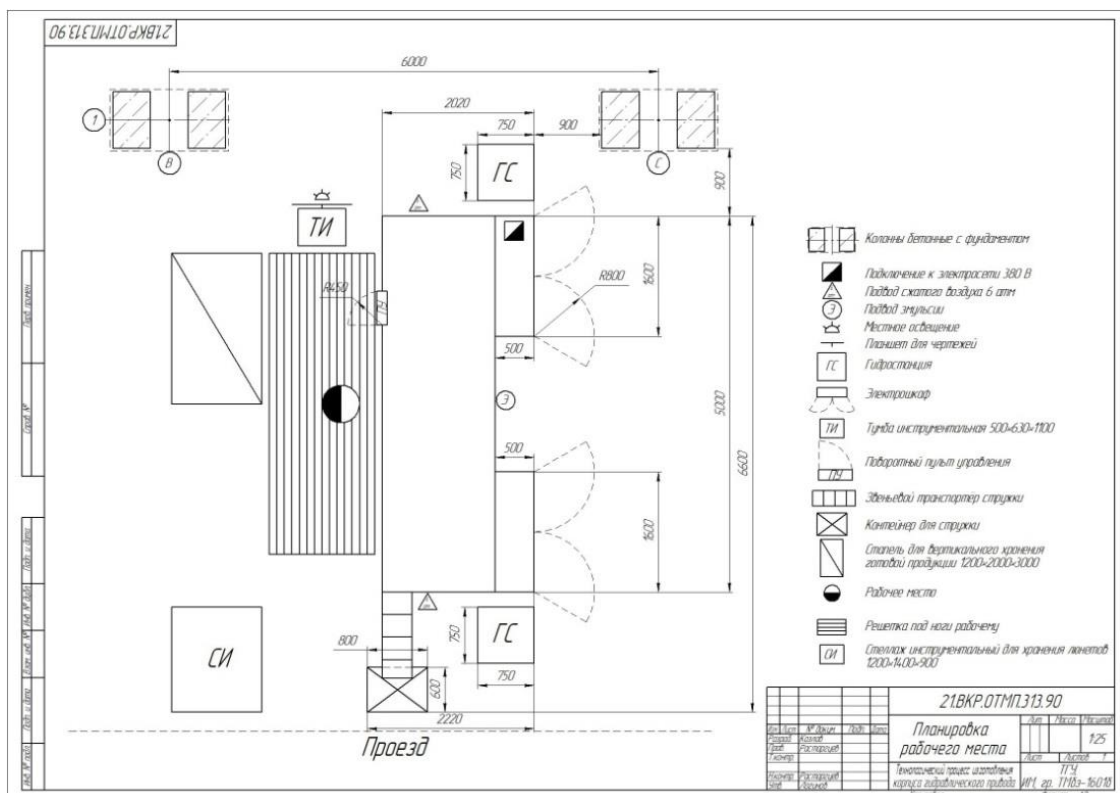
Участок обработки корпуса привода в виде втулки
